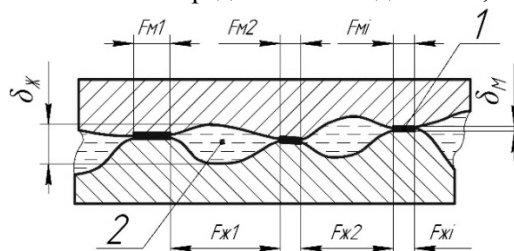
Схема зоны контакта поверхностей инструмента и детали:
